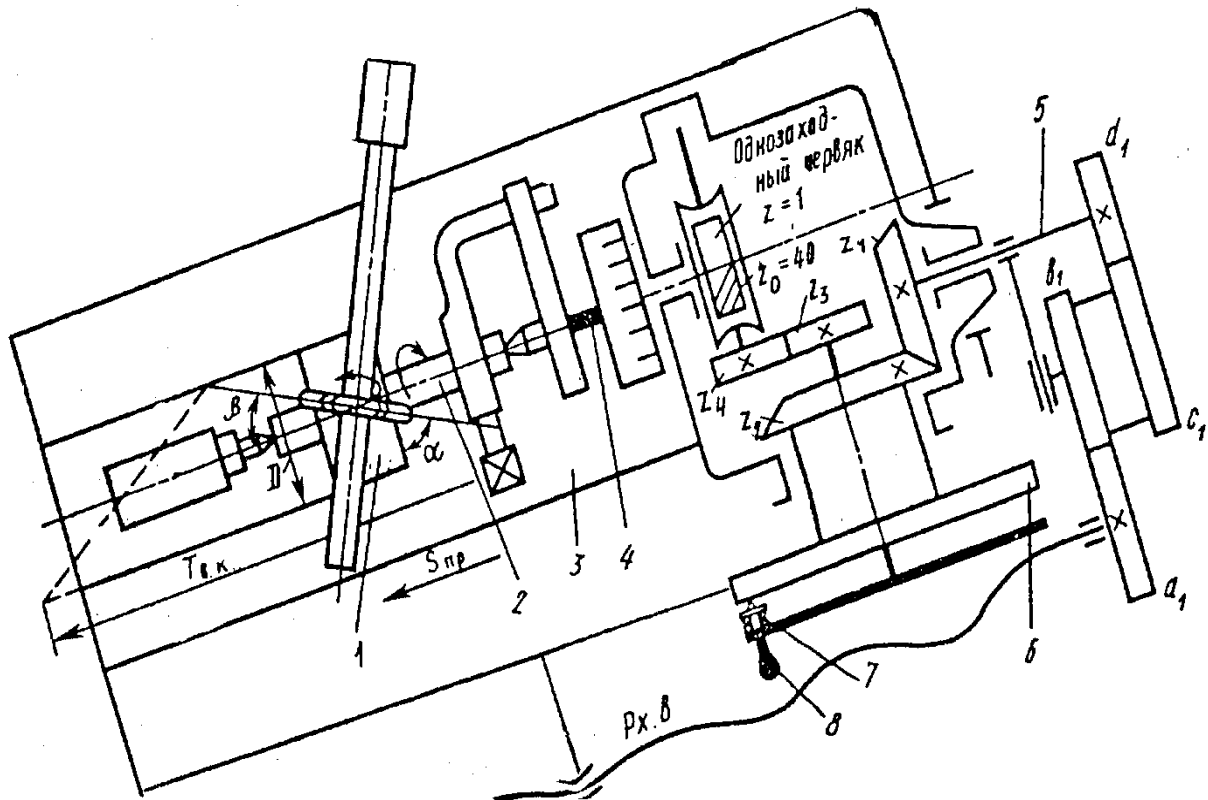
Схеми налагодження універсально-фрезерного верстата та ділильної головки на фрезерування гвинтових канавок:
